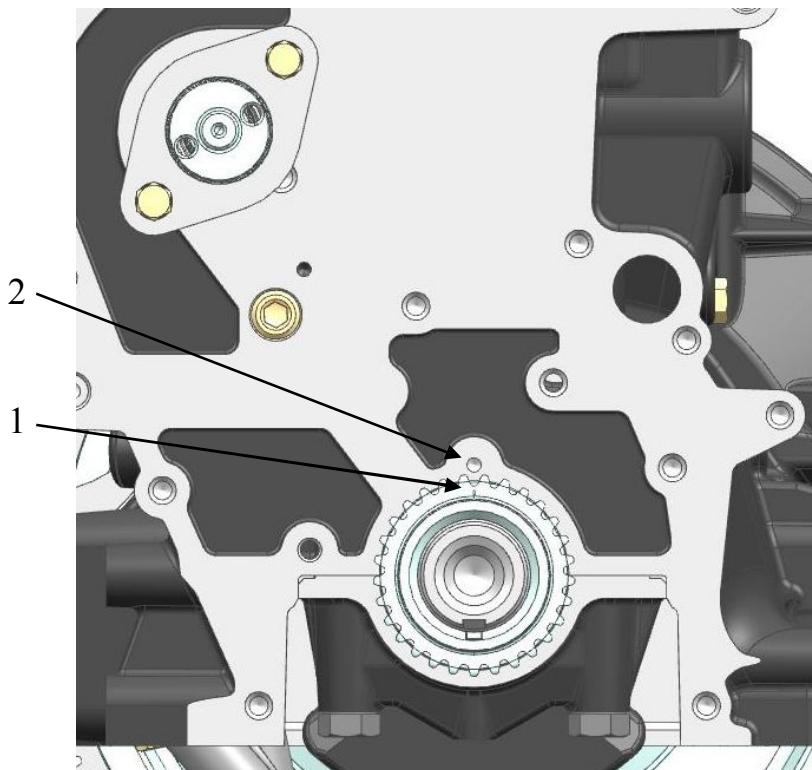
Метки блока цилиндров и звездочки коленчатого вала:
